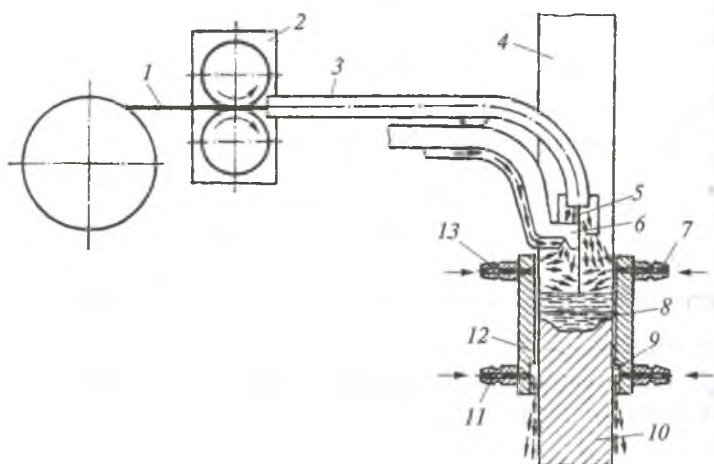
Схема приспособления типа А-1022 для электрошлаковой сварки изделий из титановых сплавов проволочными электродами:
